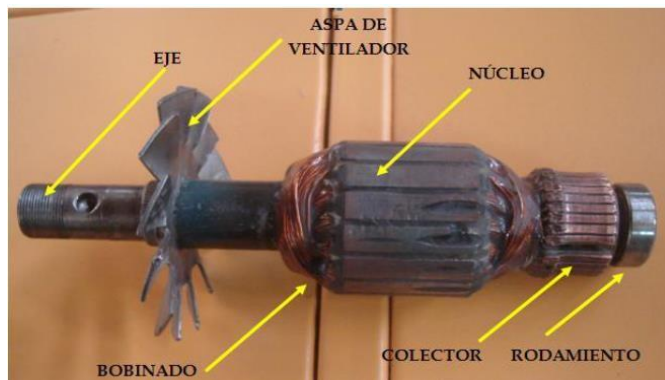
Partes principales del rotor de bobinado Fuente: Francisco, Cánovas & Molina, 2011.
